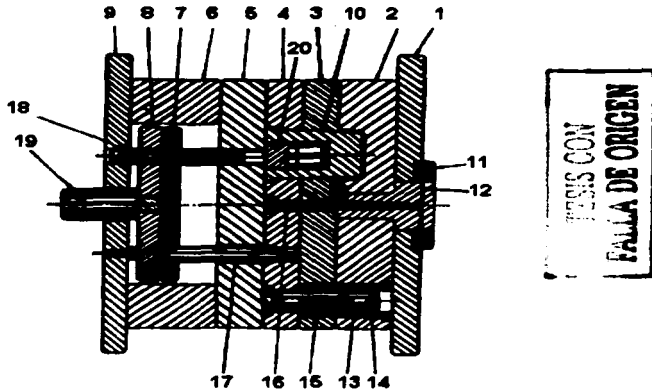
Moldes Simples (Nomenclatura). 1) Placa de fijación del lado estacionario. 2) Placa de cavidad. 3) Placa desmoldadora. 4) Placa de macho. 5) Placa de soporte. 6) Bloque espaciador. 7) Placa superior de eyector. 8) Placa inferior de eyector. 9) Placa de fijación del lado móvil. 10) Macho. 11) Centrador del molde. 12) Manguito del bebedero. 13) Perno guía. 14) y 15) Manguito del perno guía. 16) pasador enclavador de bebedero. 17) Pasador de retorno. 18) Pasador de guía. 19) Barra eyectora. 20) Atemperado del molde.
